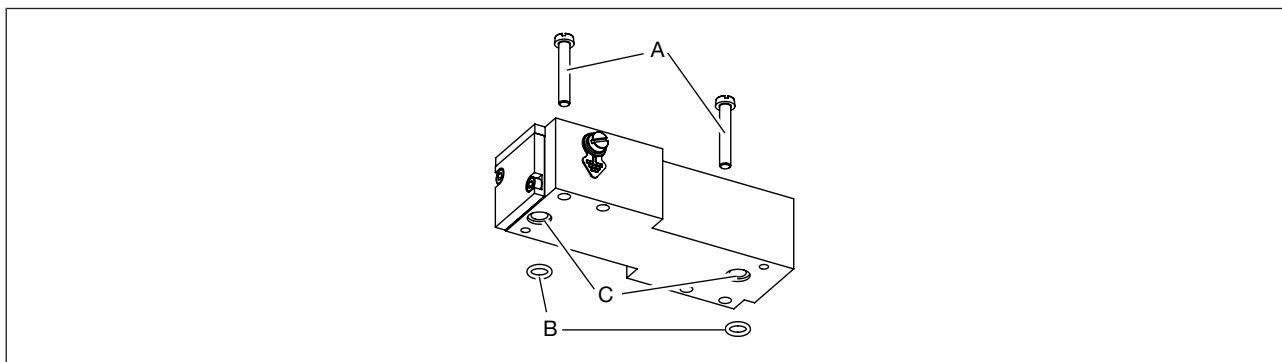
Collegamento flangia con viti e guarnizione O-ring
